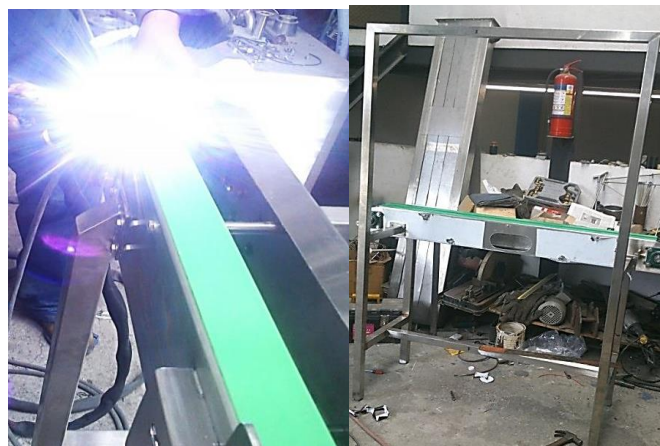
6 Soldadura y ensamblaje de la estructura
